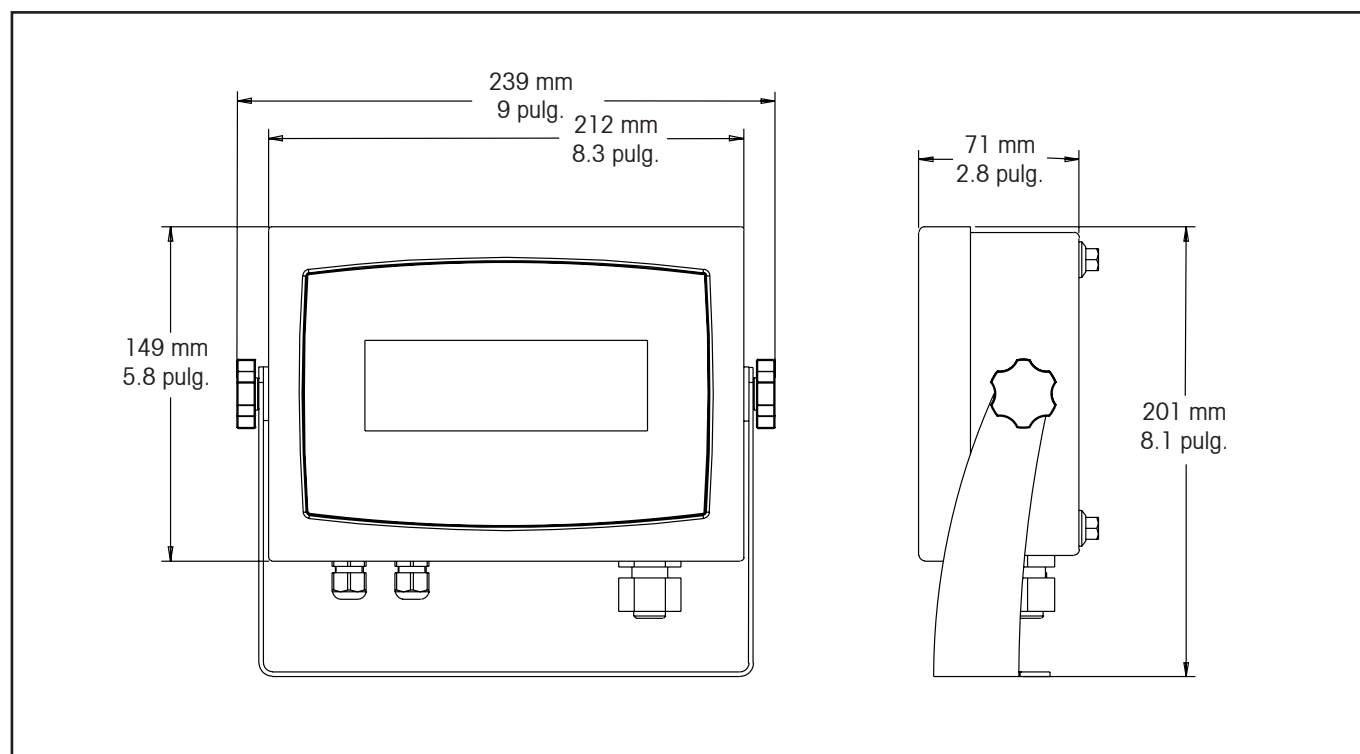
Dimensiones generales del indicador T31XW con soporte de montaje.
